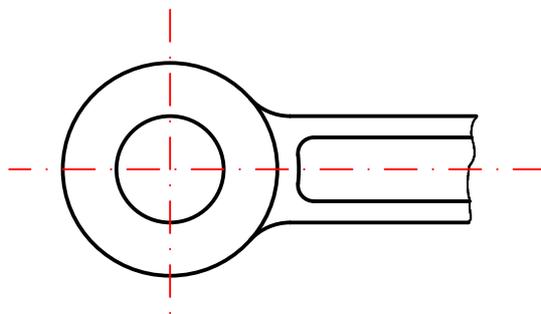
Beispiel Anwendung des Freihand Linien Werkzeugs.
